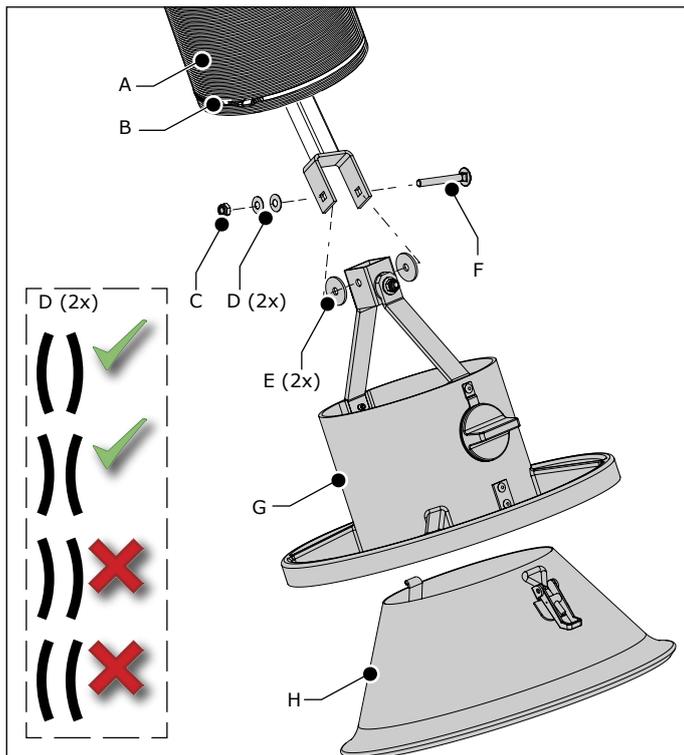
Montaje de la campana (brazo de tubo manguera)
